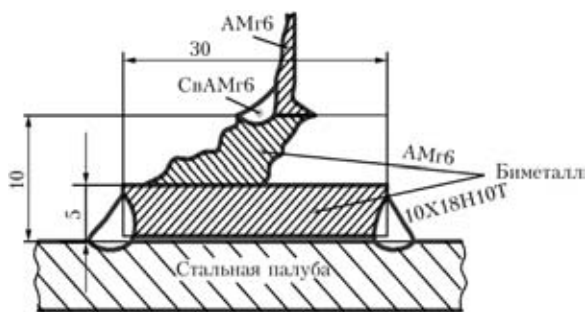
Эскиз сварного биметаллического соединения после воздействия морской среды
